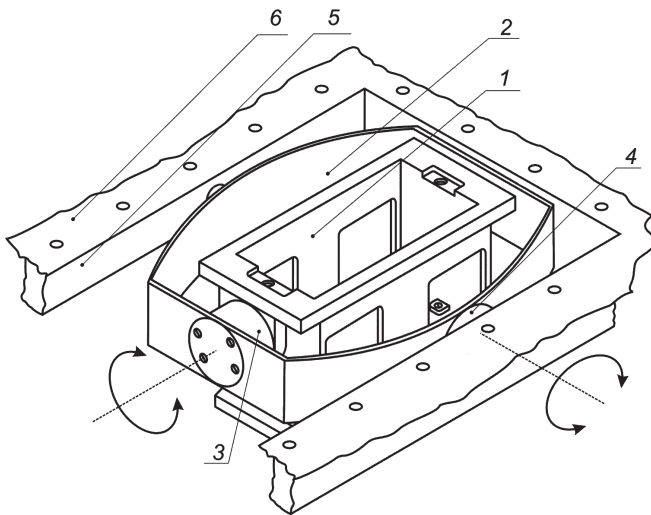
Устройство выброса АЭЗ: 1 — корпус коробчатой формы; 2 — рамка; 3 — механизм поворота корпуса; 4 — механизм поворота рамки; 5 — силовой элемент фюзеляжа; 6 — обшивка фюзеляжа летательного аппарата
